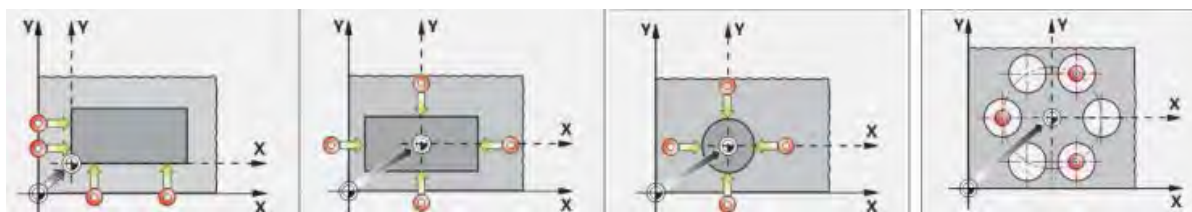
Привязка начальной точки к детали на станке с использованием её геометрических элементов
